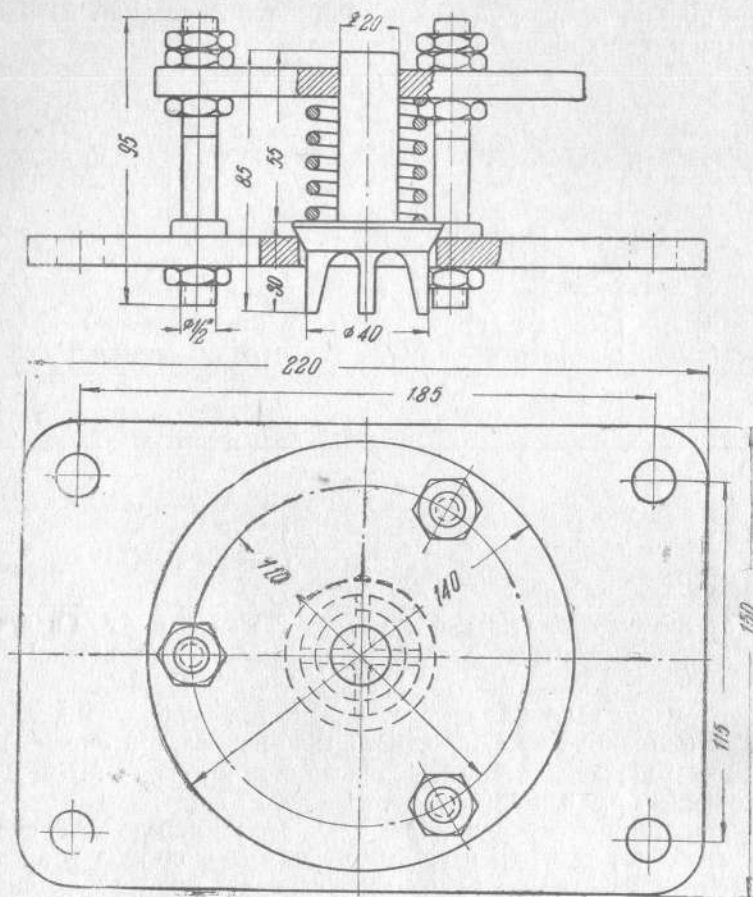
Предохранительный клапан газогенераторной установки Дубовского
